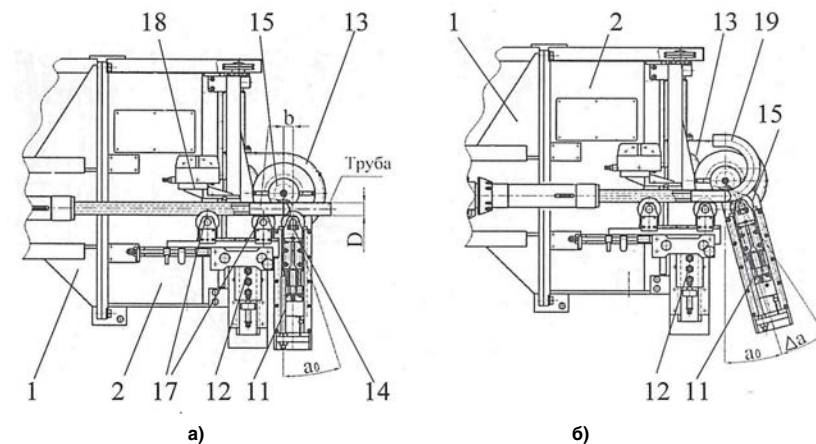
Работа гибочной головки станка в режиме проталкивания трубной заготовки через сменный опорный гибочный шаблон: а) гибочный шаблон минимального диаметра, исходное положение; б) гибочный шаблон минимального диаметра, конечное положение;  $\alpha$  — угол поворота отклоняющего ролика,  $\Delta\alpha$  — угол поворота отклоняющего ролика,  $b$  — начальное плечогиба,  $D$  — наружный диаметр трубы
